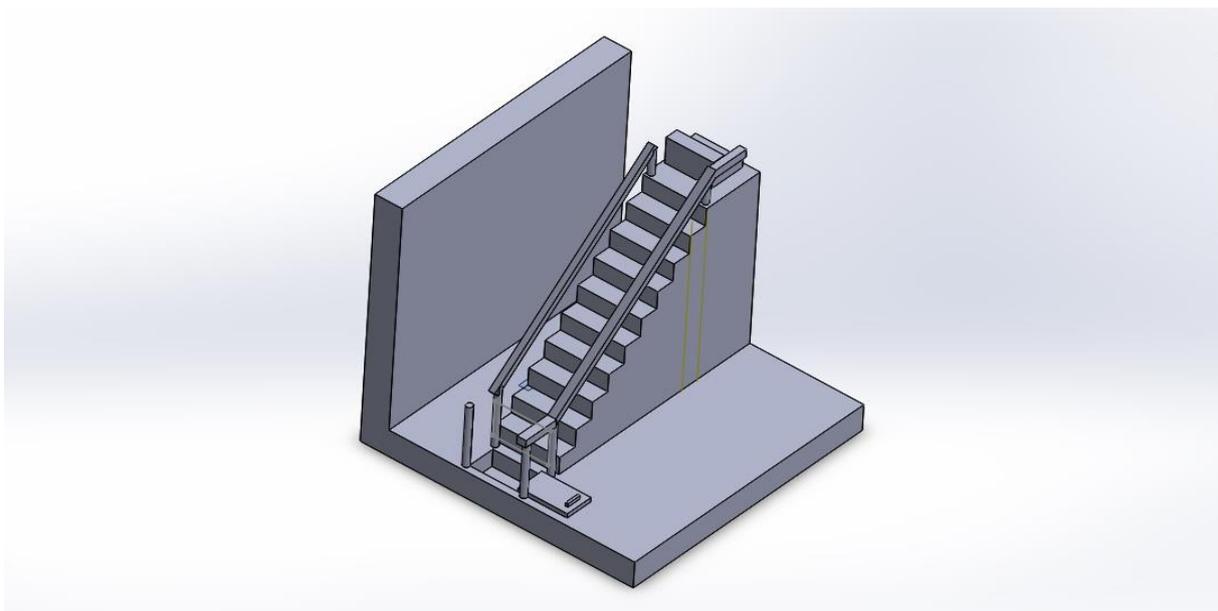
Chaise monte-escalier Glissante sur deux rails pour un escalier central.
